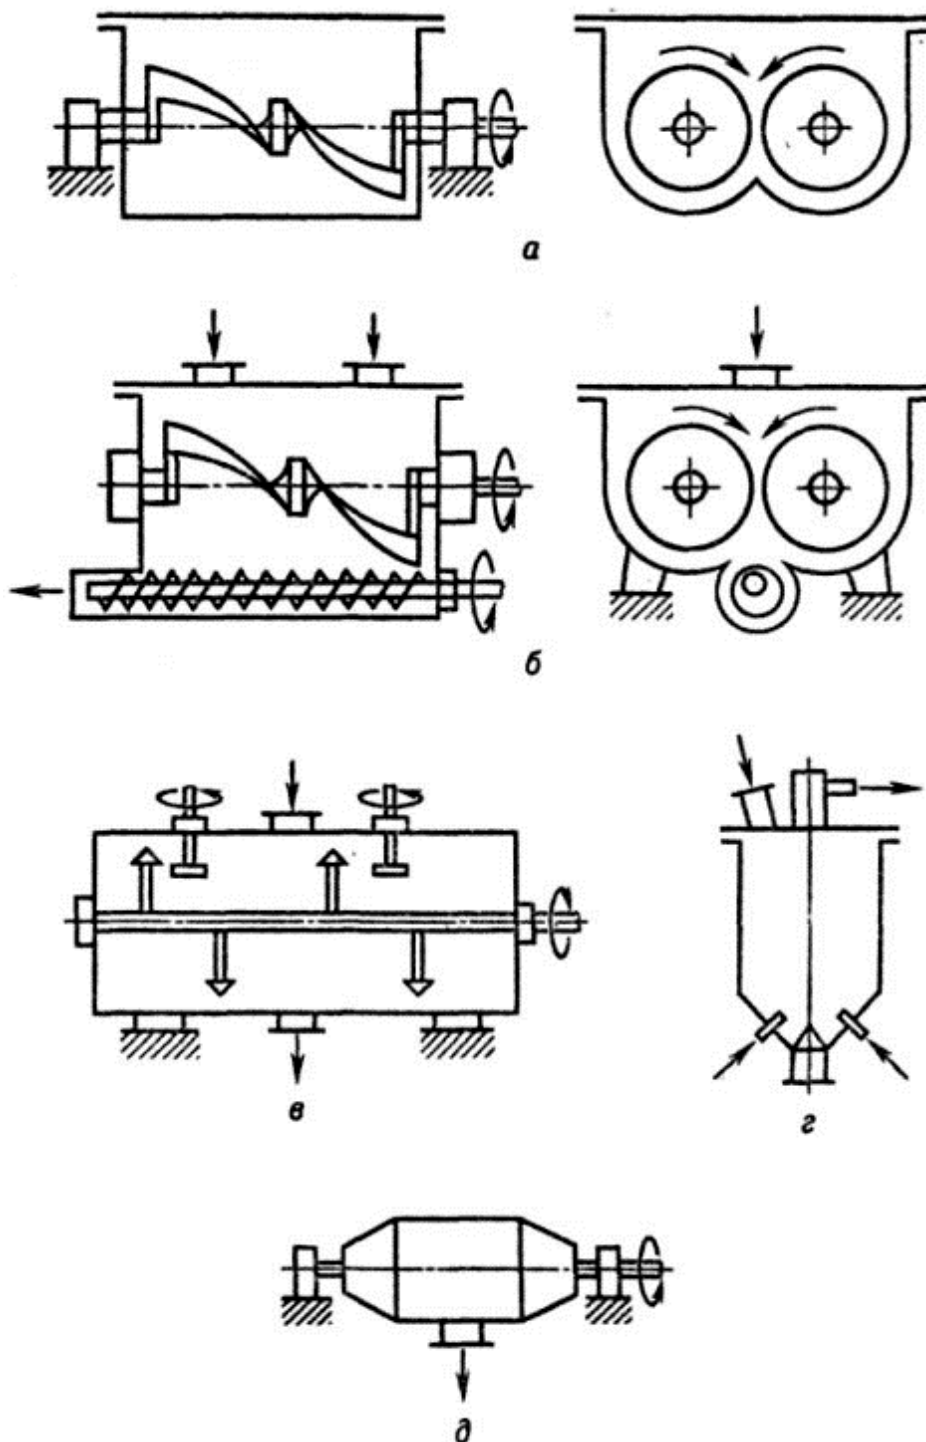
Апарати об'ємного змішування: а - з Z - образними лопатями; б - з Z-образними лопатями і розвантажувальним шнеком; в-плужний; г - пневматичний сопловий; д - барабанний
